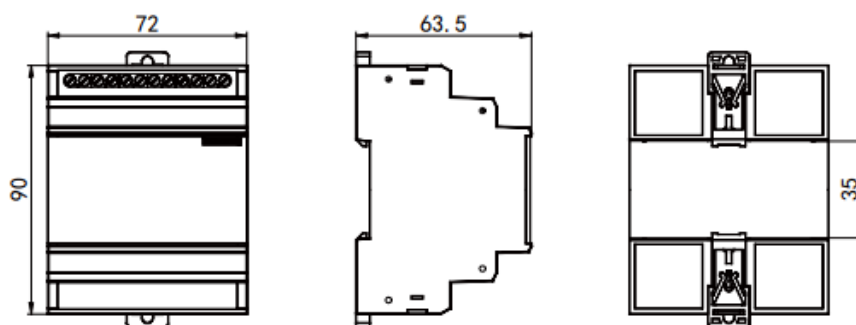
Внешний вид и габаритные размеры модуля измерительного КСМ-М1-2 и КСМ-М1-4
